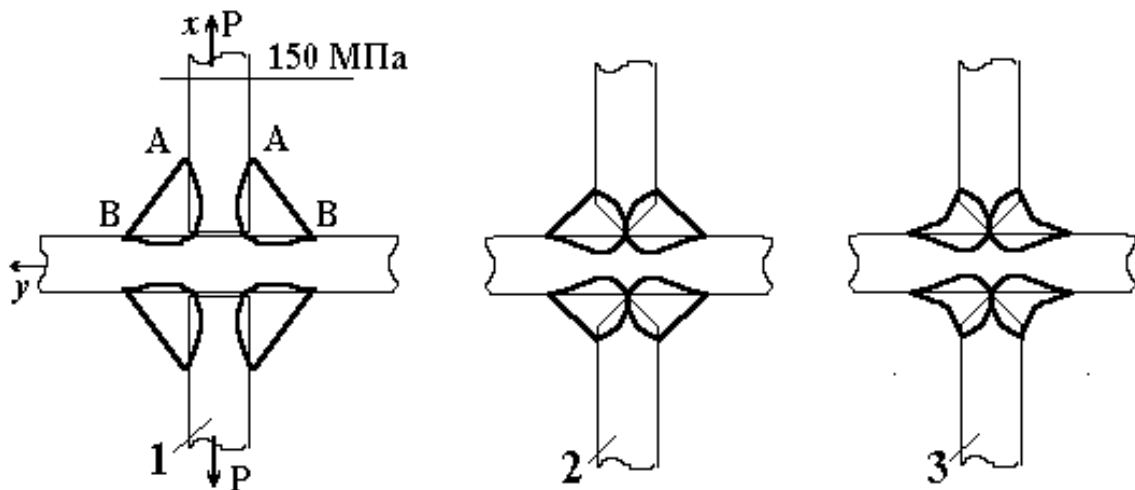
Форми хрестоподібних зварних з'єднань «впритул»
